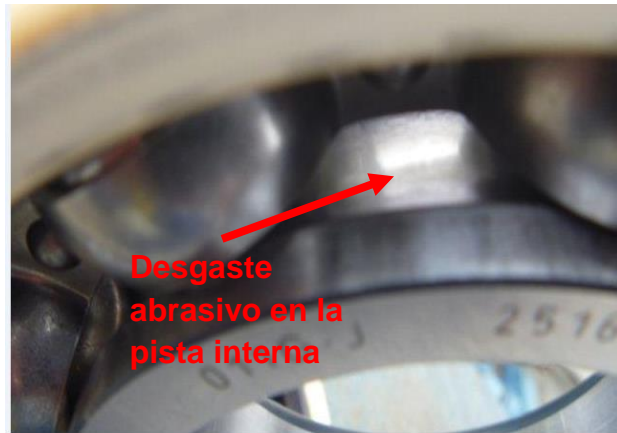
foto del rodamiento lado de la tapa del motor
